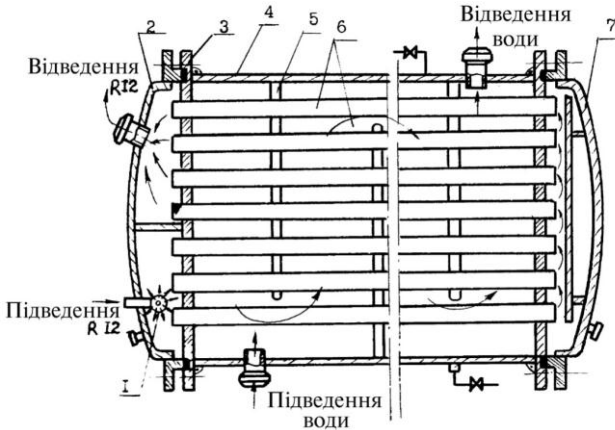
Схема фреонового випарника типу ИТ із внутрішнім кипінням R12: 1 - форсунка; 2- кришка; 3 - трубні решітки; 4 - обечайка; 5 - перегородки; 6 - мідні трубки; 7 - кришка.
